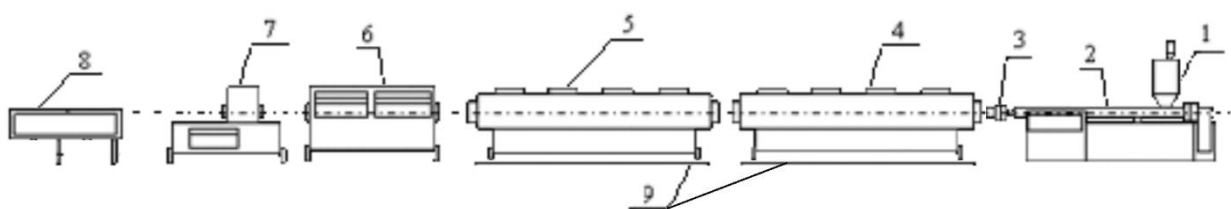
Схема екструзійної лінії для виготовлення труб
